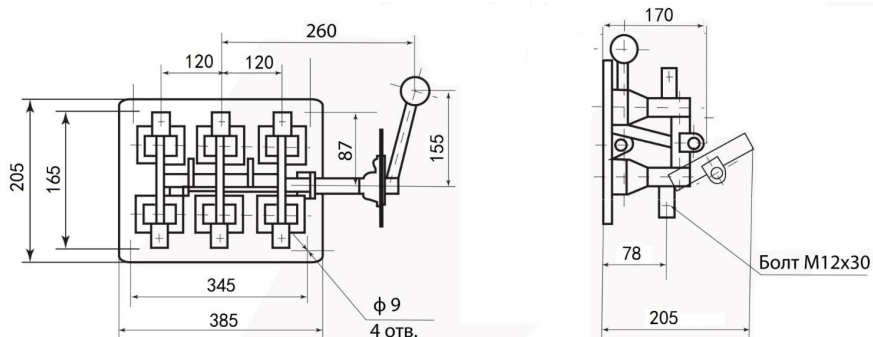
Разъединитель серии Р с боковой рукояткой РБ-1, РБ-2 на номинальные токи 100 А и 250 А
